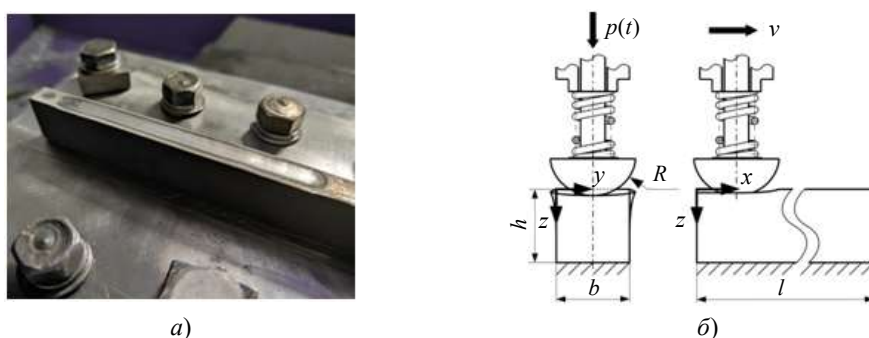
Контрольный образец (а), прокованный пневмомолотком, и схема процесса (б)
